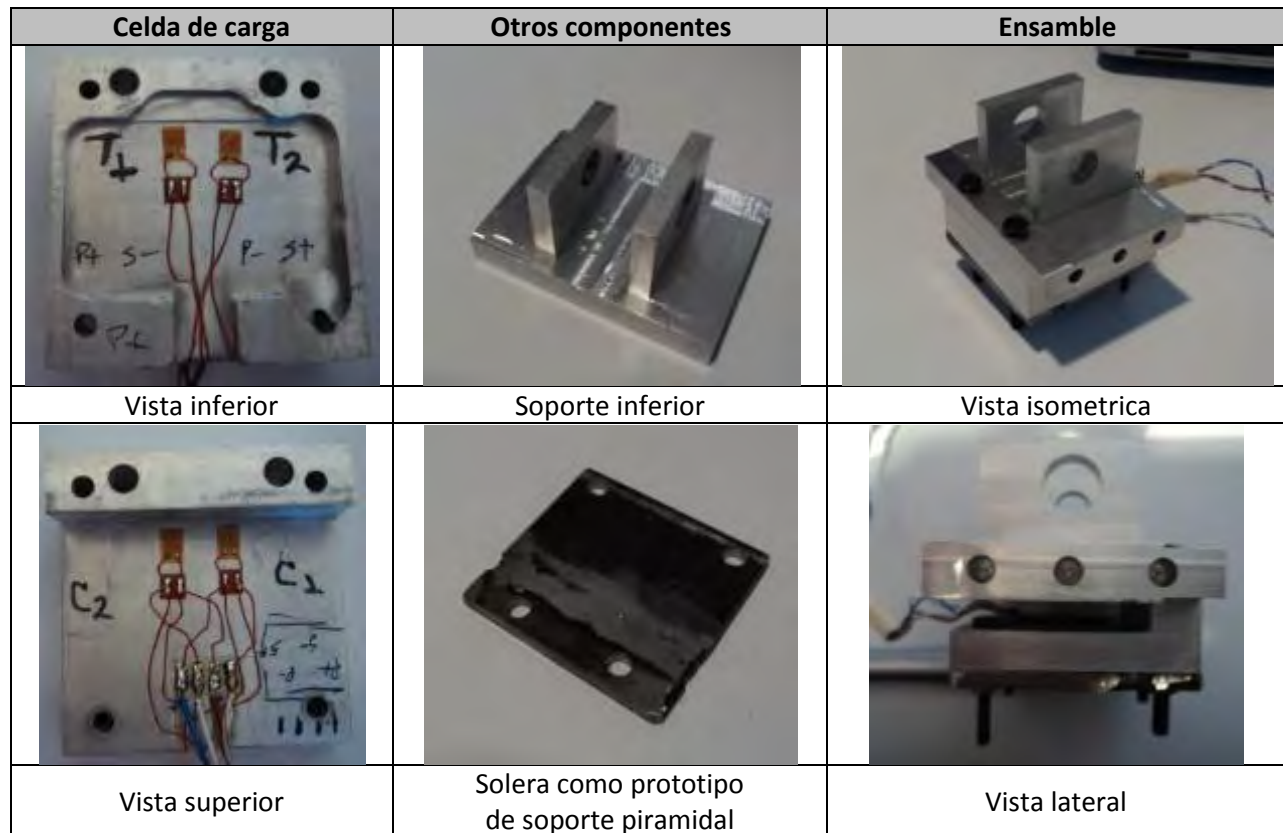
Construcción del ensamblaje para la instrumentación de galgas extensométricas.
